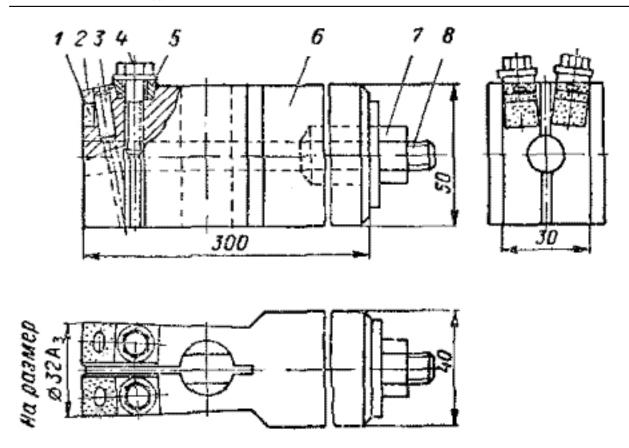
Калибровочный резец с четырехгранными пластинками.
